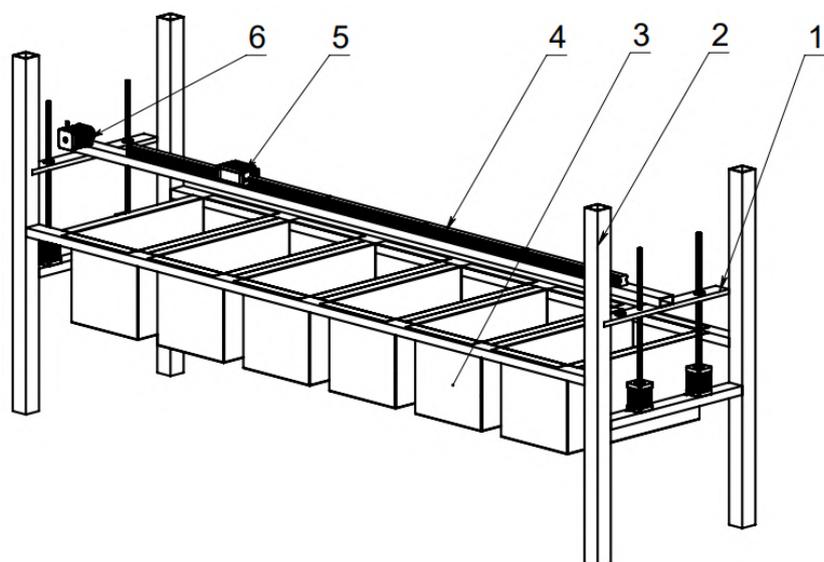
Изометрия декартового модуля. 1 – кинематическая основа, 2 – рама, 3 – ванны, 4 – рельс, 5 – направляющий подшипник, 6 – шаговый двигатель
